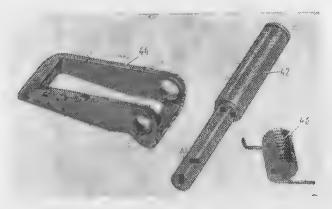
Детали стопора лотка: 42 — ось 2А26.02-163; 43 — пружина 2А26.02-162; 44 — стопор 2А26.02-161 или 2А26.02-161-1
